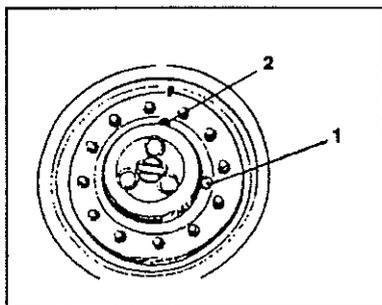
Engranaje planetario / posición de llenado de aceite
